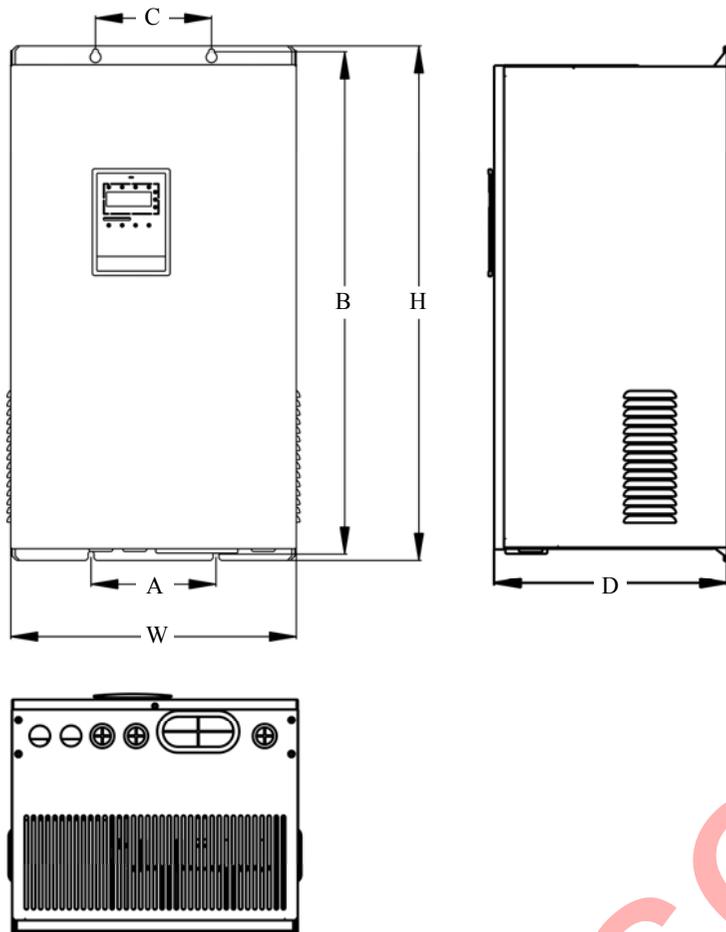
Габаритные и установочные размеры блоков торможения
